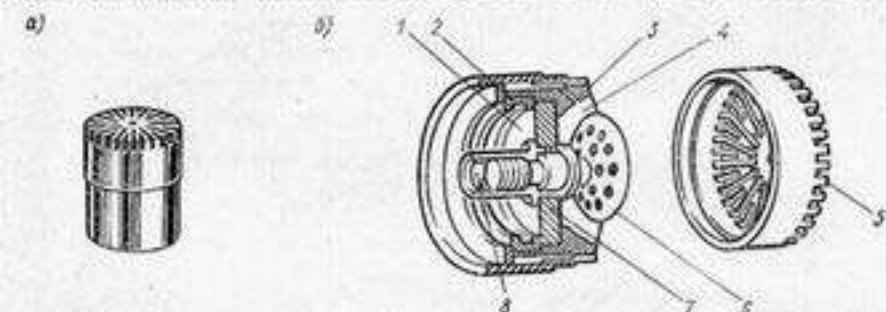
Внешний вид (а) и конструкция (б) конденсаторного микрофона. 1 — пружина; 2 — капилляр для выравнивания статического давления; 3 — регулятор капилляра; 4 — мембрана; 5 — защитная сетка; 6 — задний перфорированный электрод; 7 — изолятор; 8 — выходной контакт.
